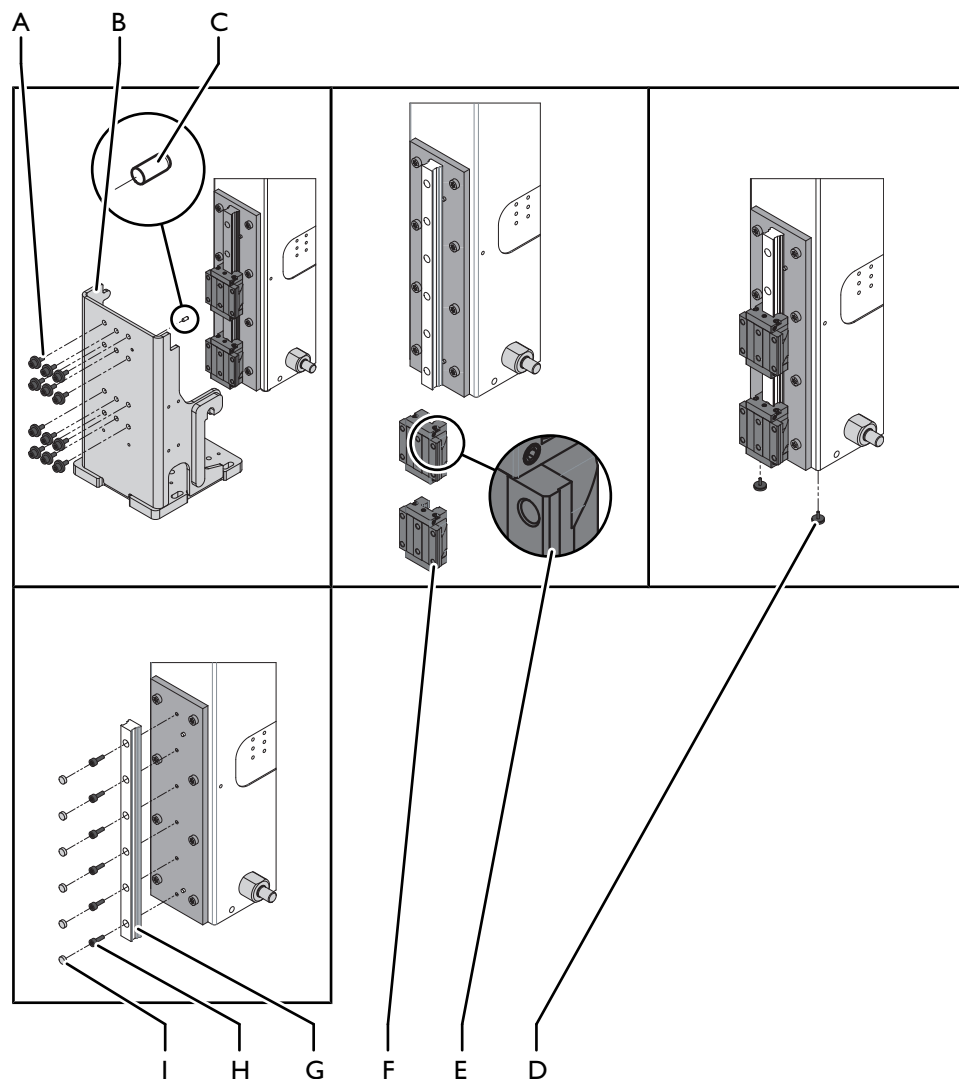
Заменить шариковую обойму, амортизатор и корпус
